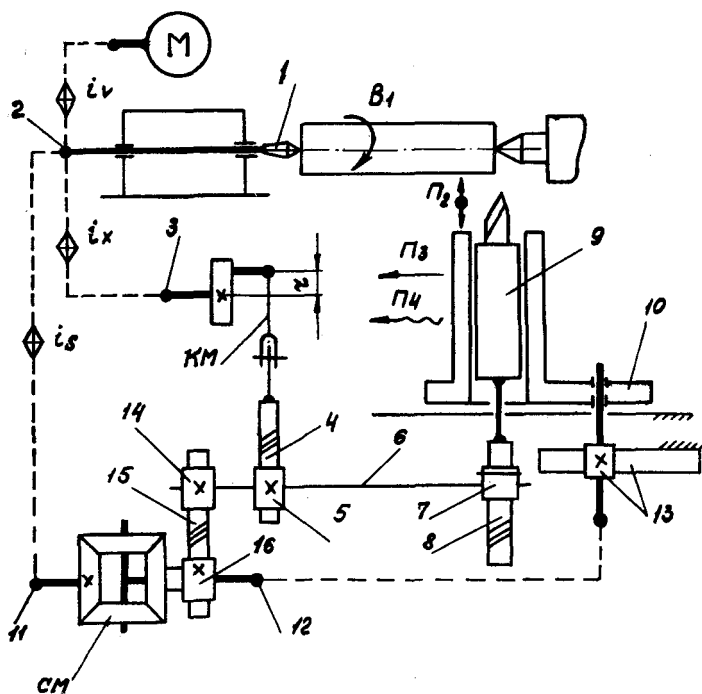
Структурная схема токарного станка для точения синусоидных поверхностей
